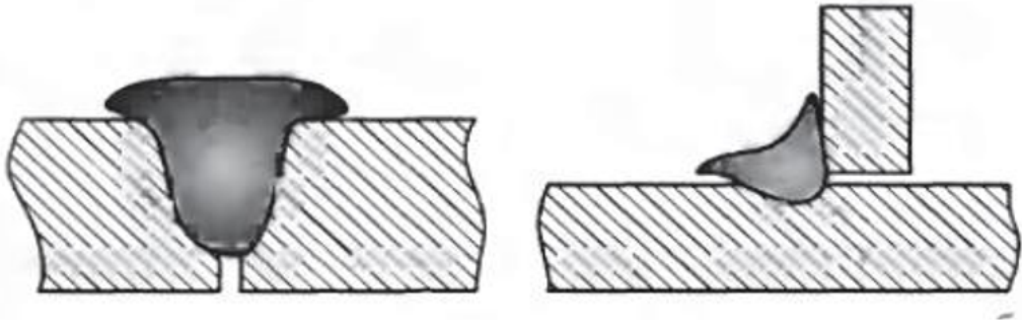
Эскиз дефекта сварного шва
